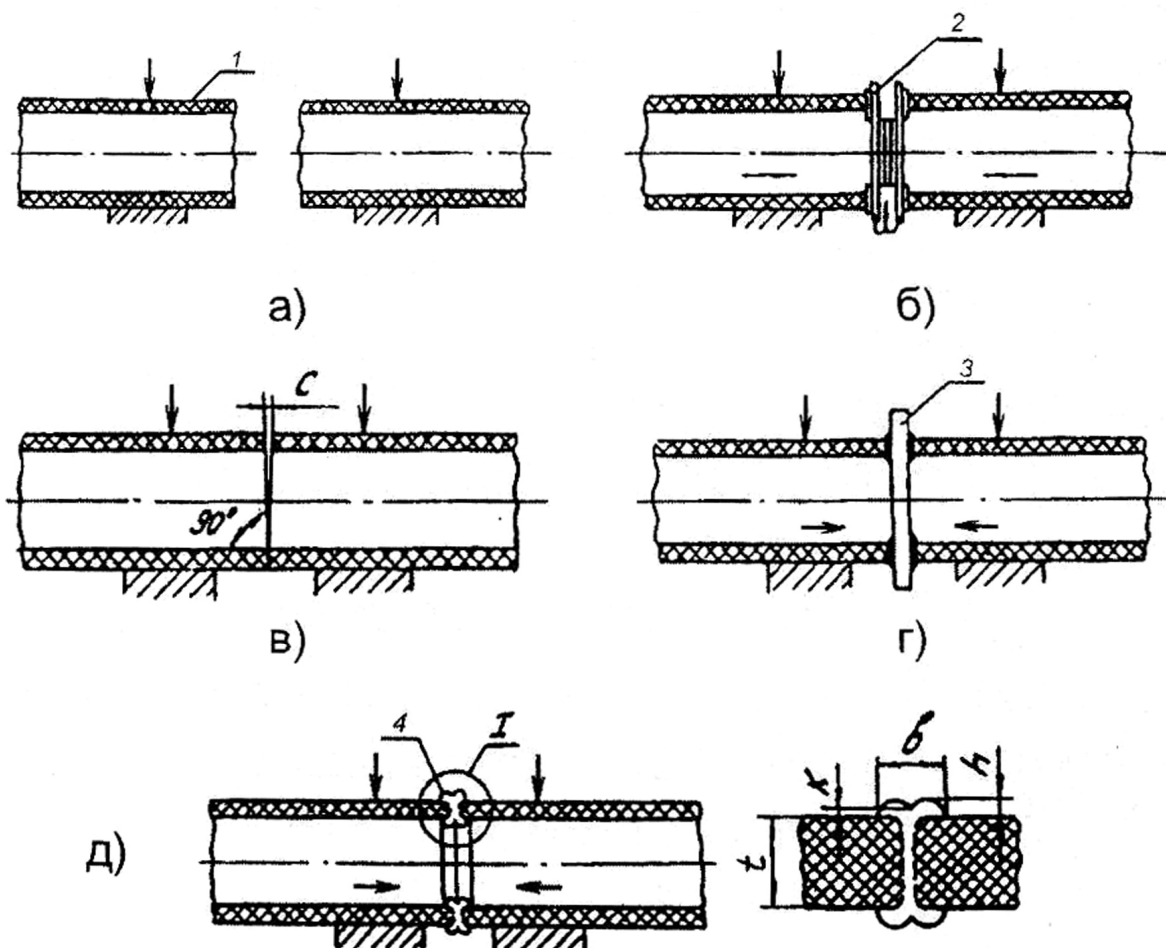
Последовательность процесса сборки и сварки встык:
